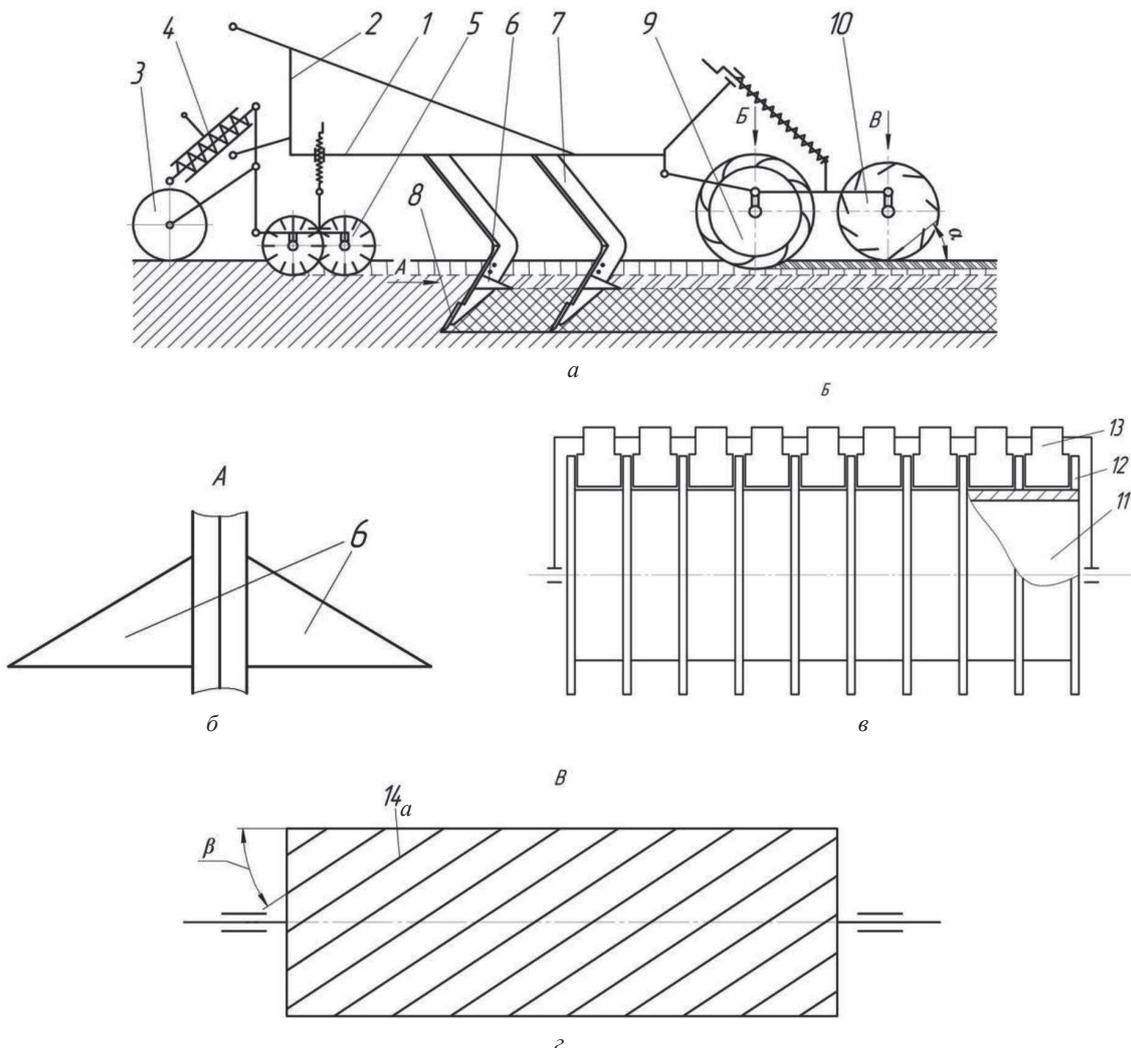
Схема комбинированного почвообрабатывающего агрегата для формирования влагосберегающего, влагонакопительного слоя почвы на склоновых землях: а – вид агрегата сбоку; б – вид А; в – вид Б; г – вид В; 1 – рама; 2 – навеска; 3 – опорные колеса; 4 – механизм регулировки; 5 – диск; 6 – лапа; 7 – стойка; 8 – долото; 9 – каток; 10 – лопастной барабан; 11 – пустотелый цилиндр; 12 – зубчатый диск; 13 – чистик; 14 – планка
